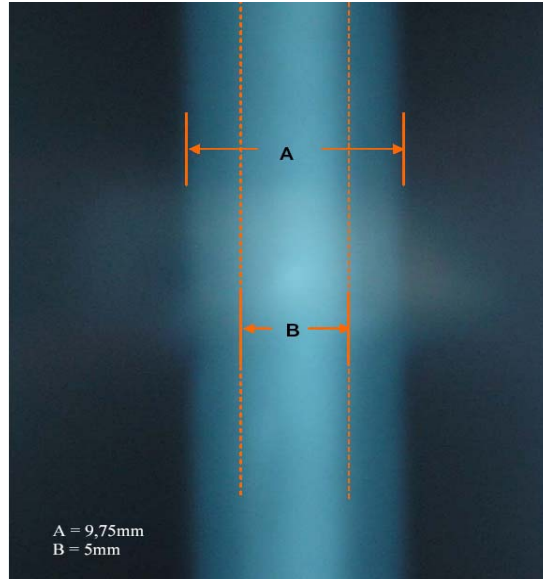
Radiografía Industrial de la Junta Soldada.
